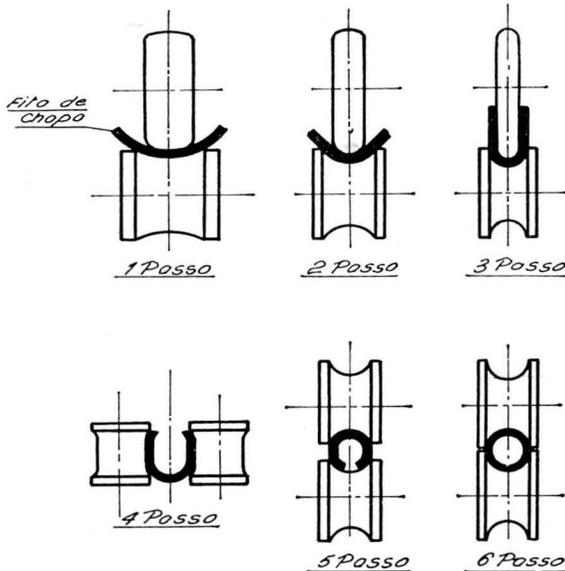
Fabricação de tubos por solda de resistência elétrica, vê-se o jogo de rolos calibradores.
